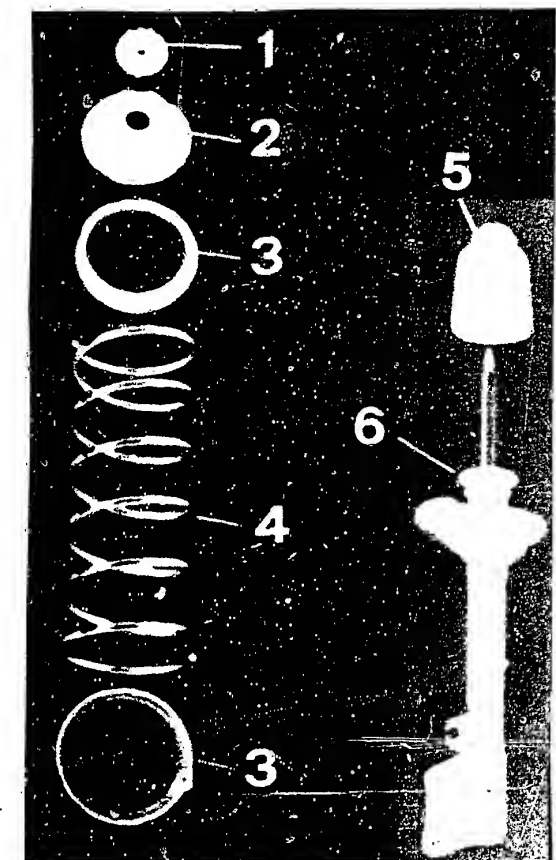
Einzelteile des hinteren Federbeins: 1 Abschlussdeckel – 2 Oberer Federteller – 3 Federauflager – 4 Feder – 5 Schutzhappe – 6 Stossdämpfer.
